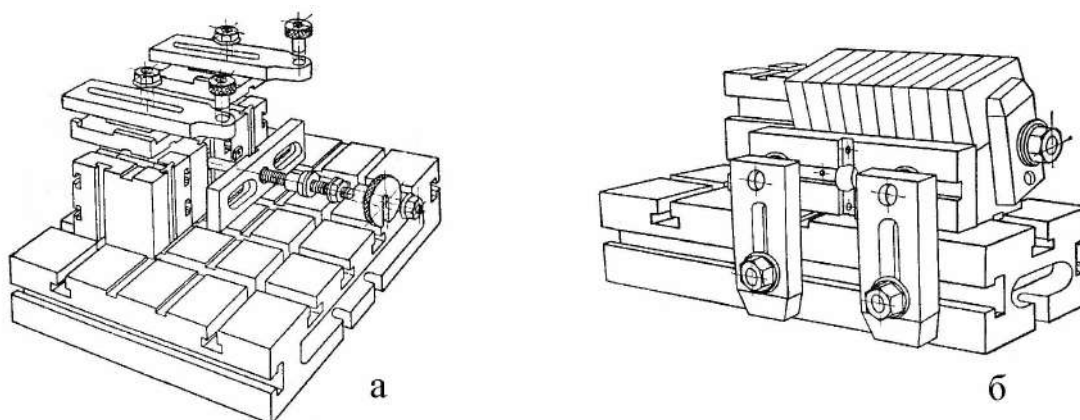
Схема компонування кондуктора (а) й стругального пристрою (б)
